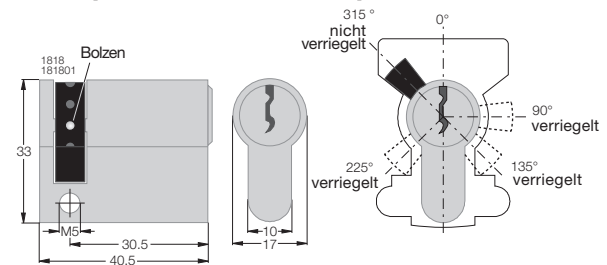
Wechselschalter 1- und 2-polig für Schließzylinder [Best.-Nr. 3826 10, 3836 20]
